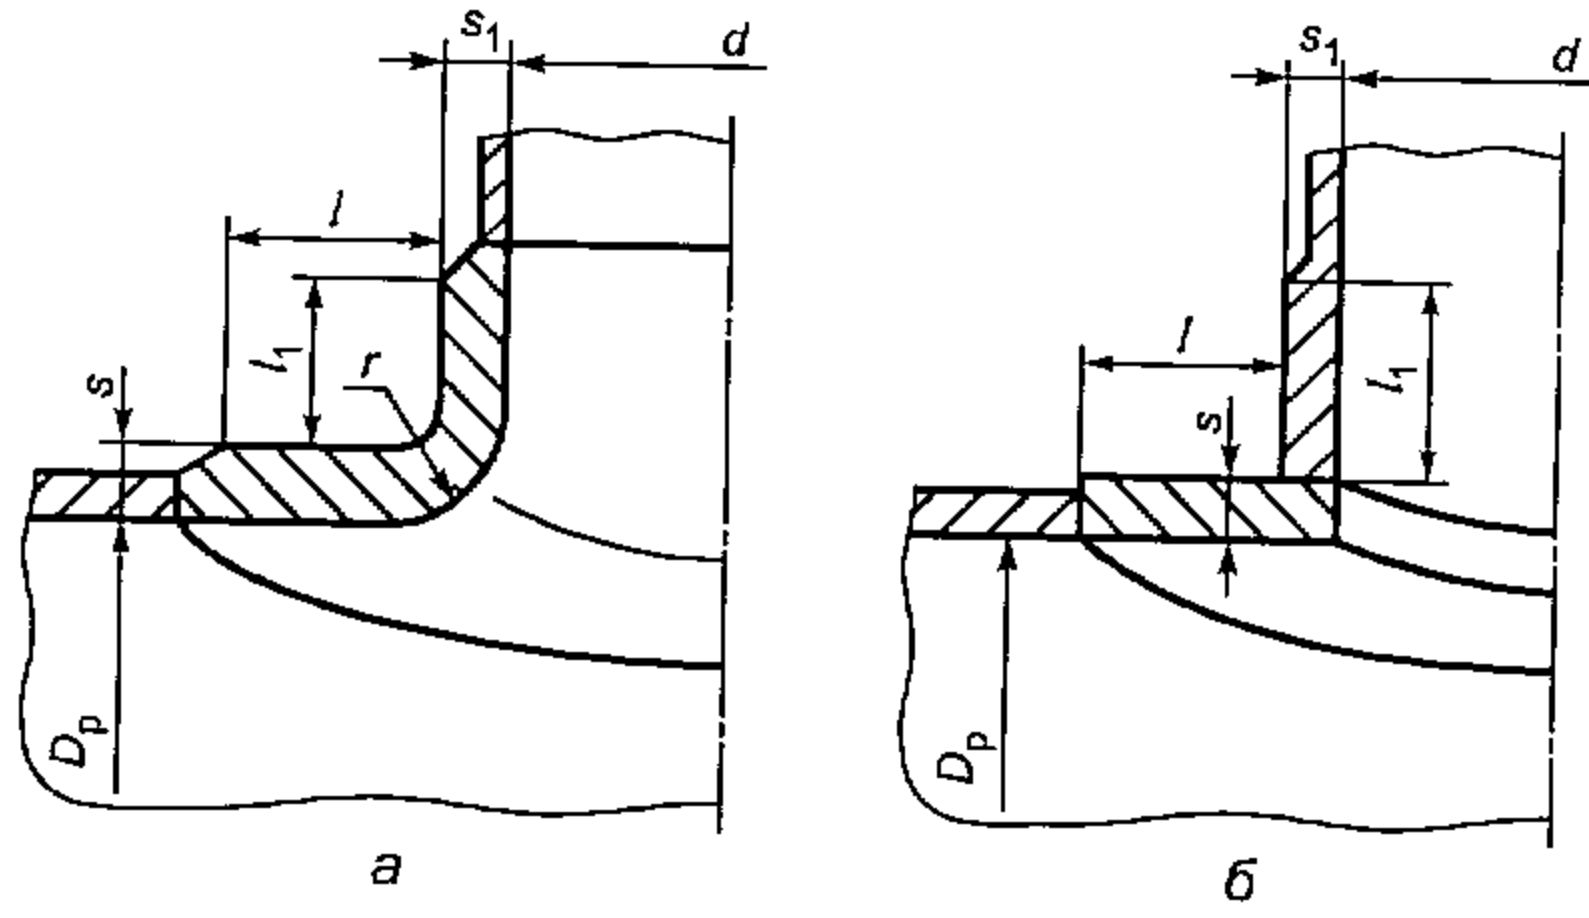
Укрепление отверстия торообразной вставкой или сварным кольцом
